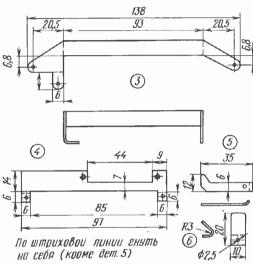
1 — несущая панель — дюралюминий 2,0 мм; 2 — пластина крепления тонвала — сталь 1,0 мм; 3 — планка узла головок — сталь 1,5 мм; 4 — стойка переключателя рода работ — сталь 1,5 мм; 6 — пружина
